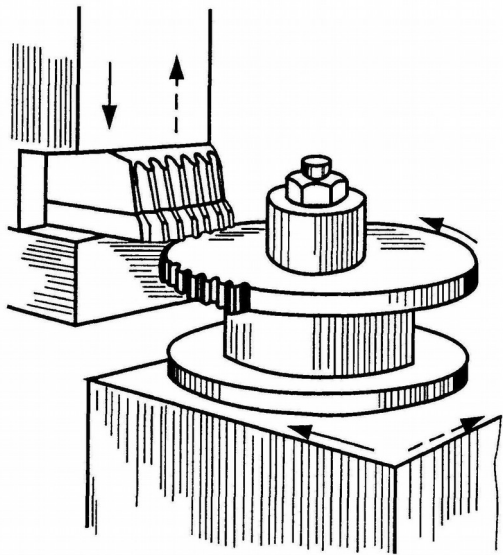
Нарізання зубчатих коліс інструментальною рейкою
